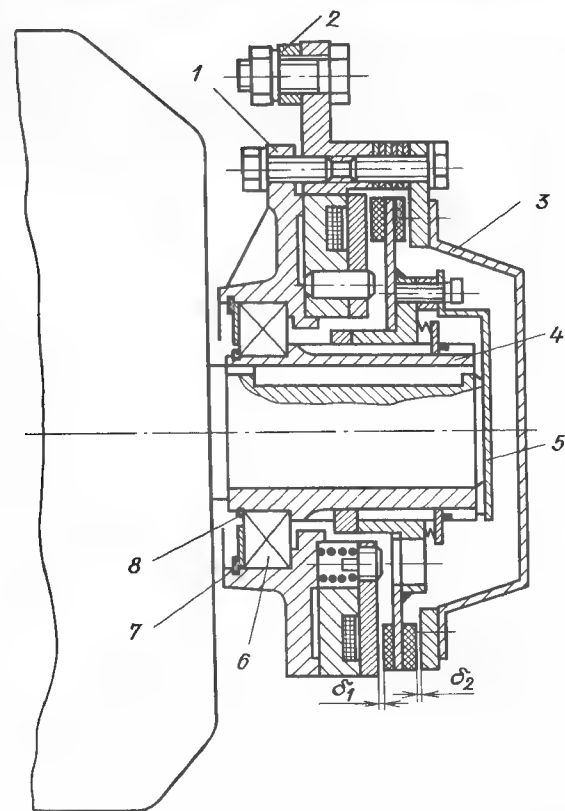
Автономный тормоз для АД серии АИ с двумя свободными концами вала
